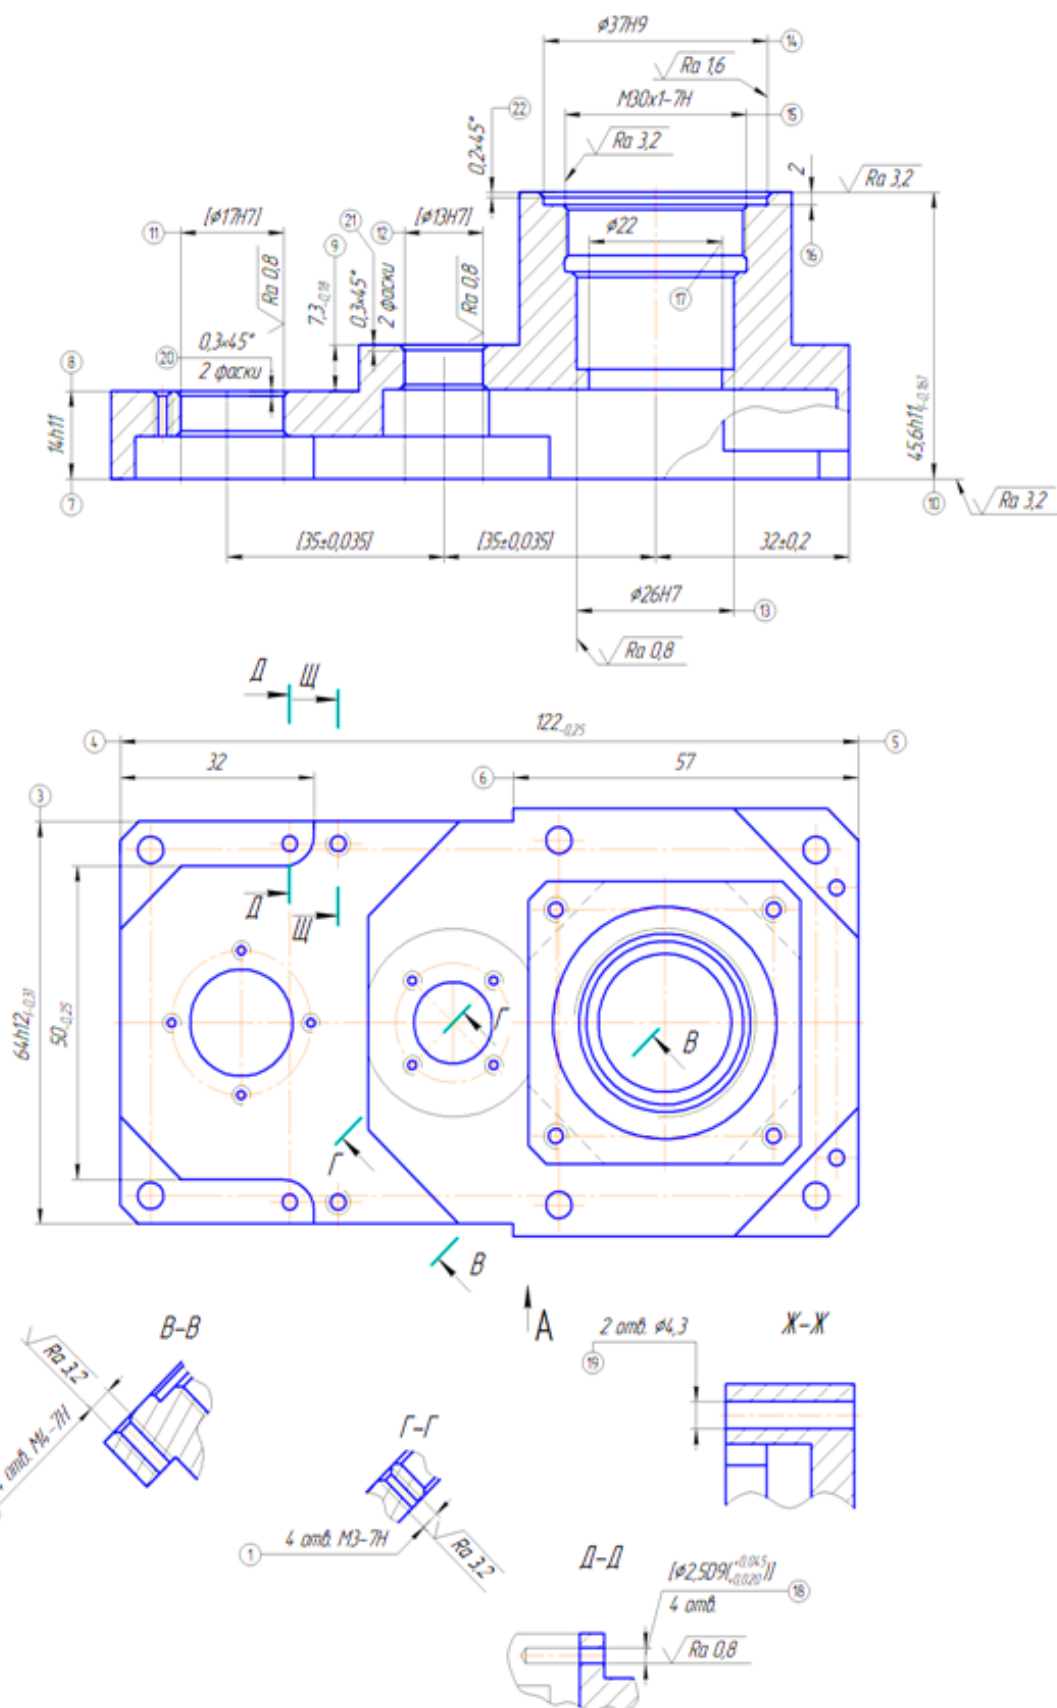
обрабатываемые поверхности детали «Крышка редуктора»
